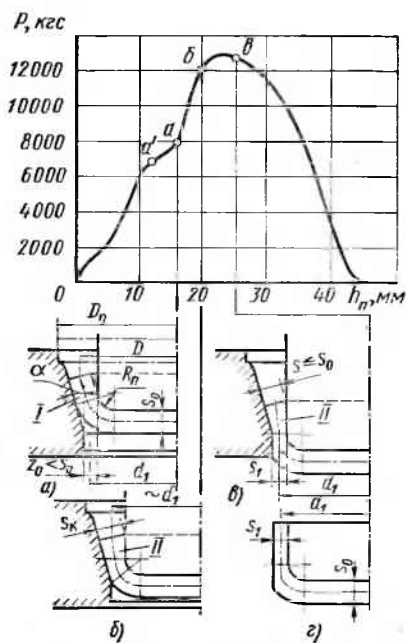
Последовательность деформирования заготовки при протяжке из плоской заготовки («свертка» с утонением)
